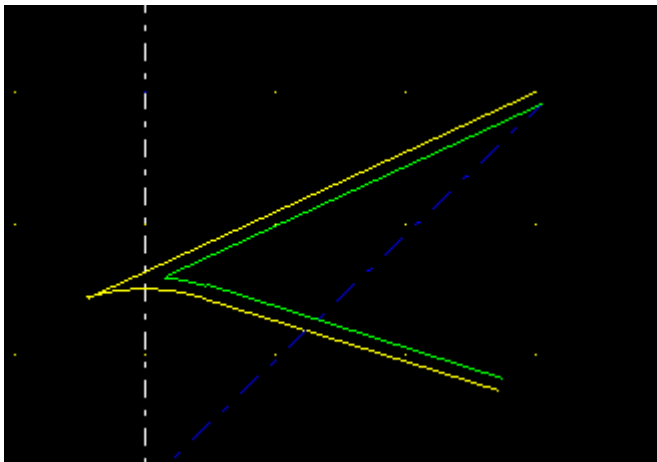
Richtige Ausgabe durch Verkleinerung des Werkzeugdurchmessers
